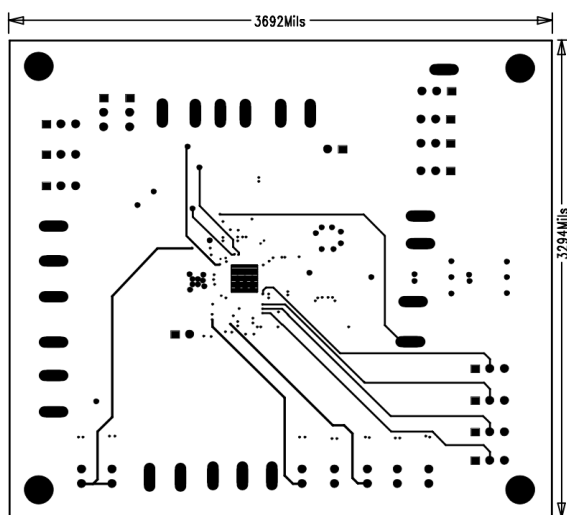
Max 8662 PCB LayOut - Routing Layer 5.
